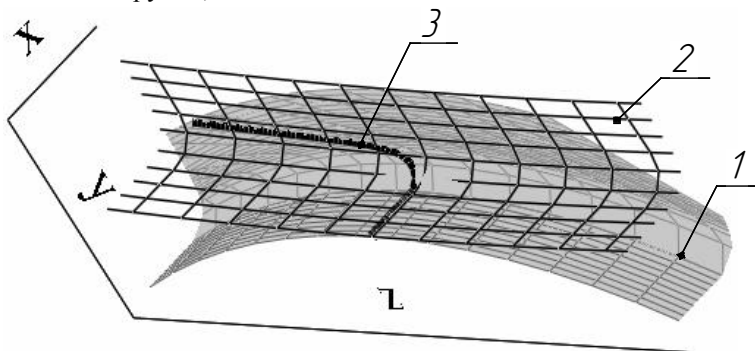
3D-модель поверхности шлифовального круга, детали и линии контакта
